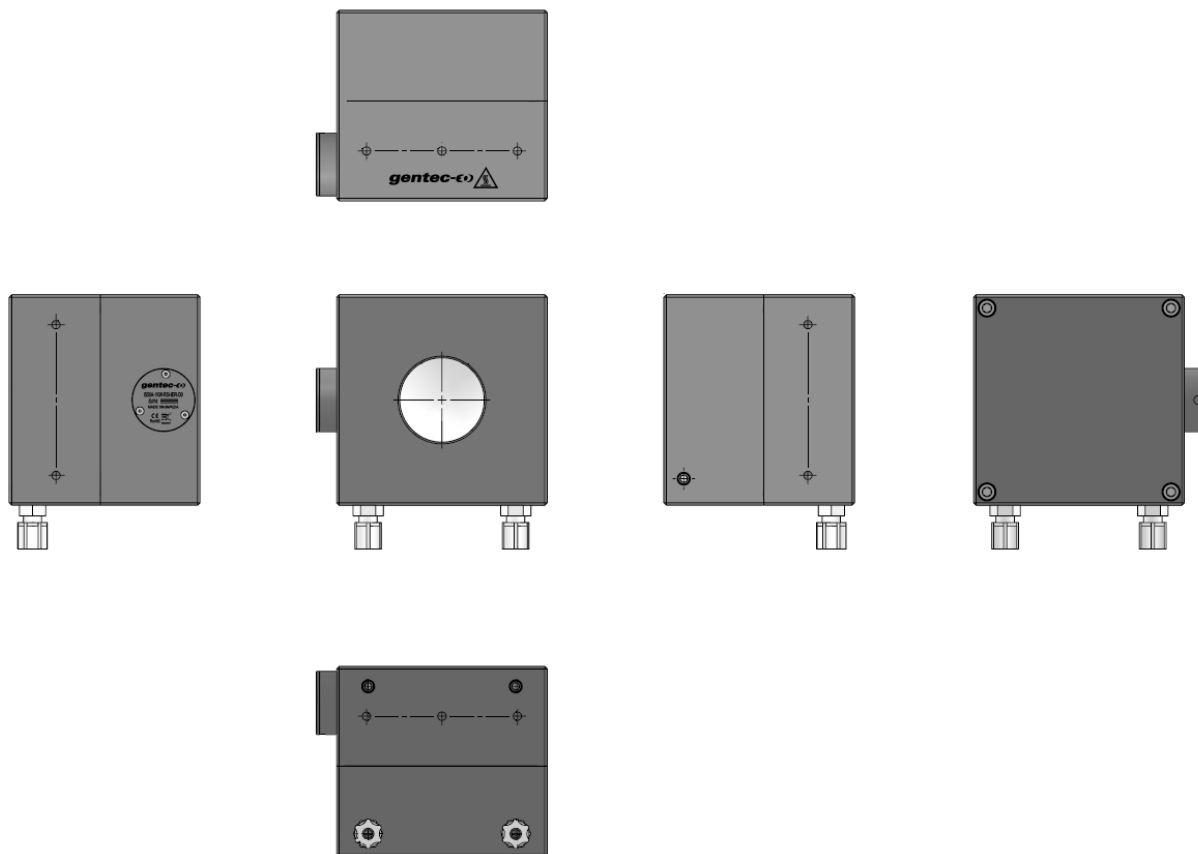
Dessin d'encombrement, IS50A-1KW-RSi-INT/IDR-D0.
